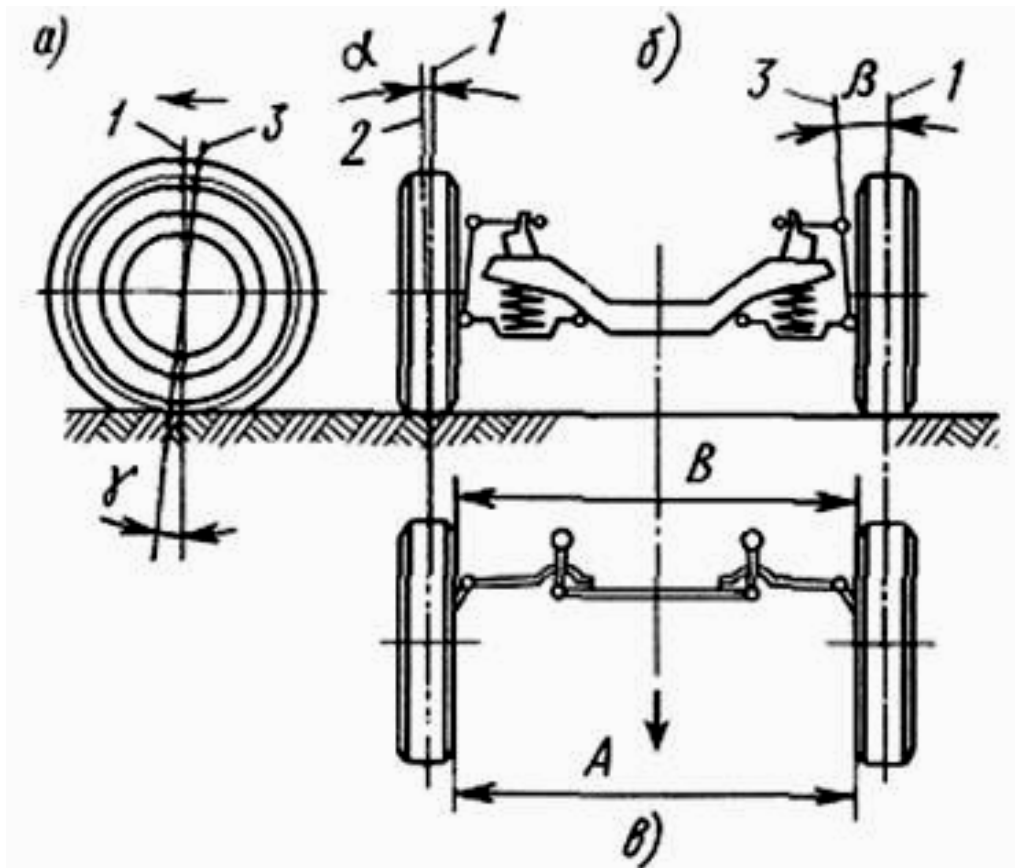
Схема углов установки передних колес в трех положениях: а - сбоку; б - спереди; в - сверху; 1 - вертикаль; 2 - плоскость вращения колес; 3 - ось поворота стойки подвески; а - угол развала колес; б - угол поперечного наклона оси стойки подвески; г - угол продольного наклона оси стойки подвески. А и В - величины схождения колес
